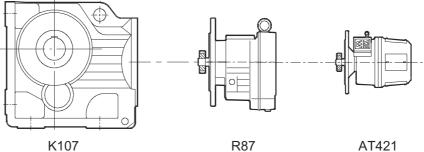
Beispiel für die Typenbezeichnung Getriebe
